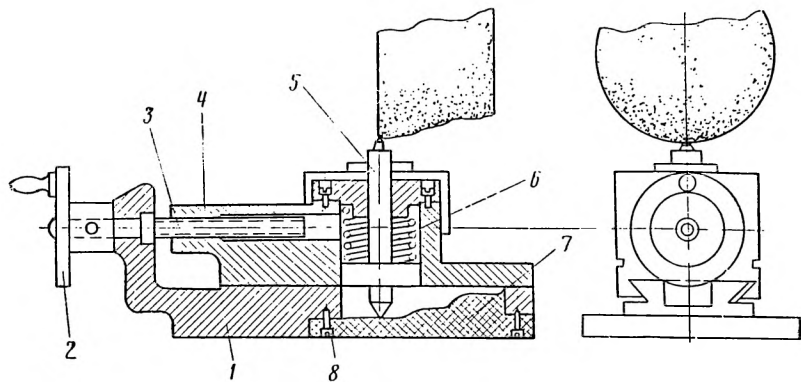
Приспособление для профилирования шлифовального круга по копии
